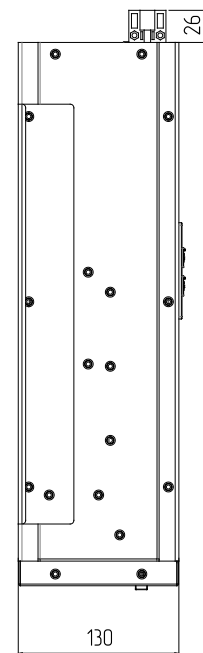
Габаритный чертеж OptiSine 30K-15A-W3, OptiSine 30K-15A-W4, размеры в мм
